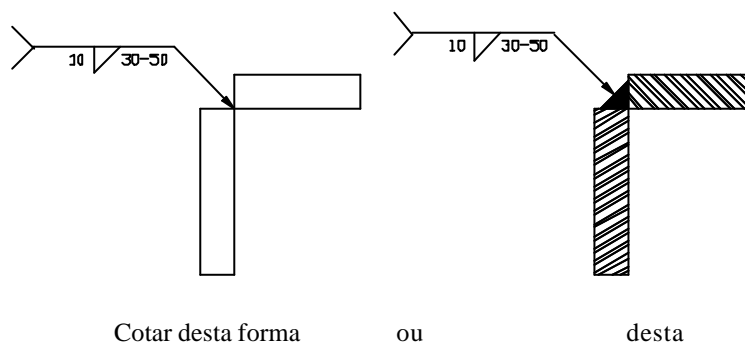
Cotagem de outro tipo de junta em “L”
